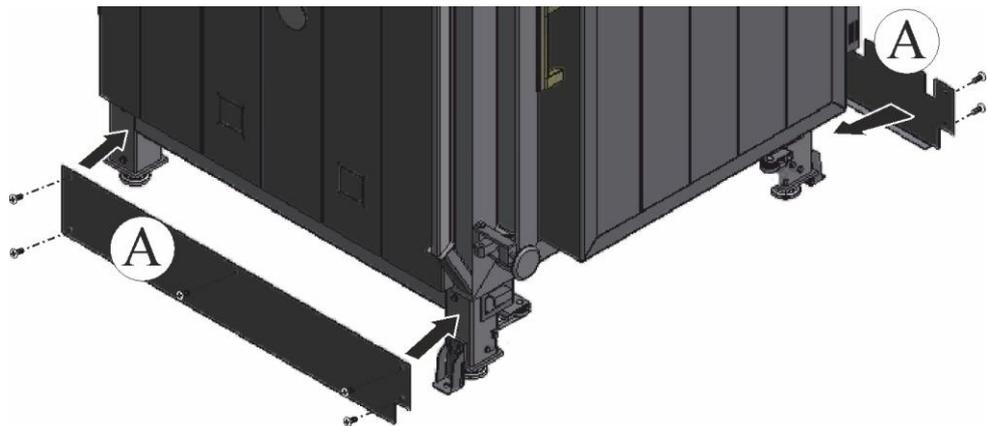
Montaggio delle lamiere laterali (figura simile)
